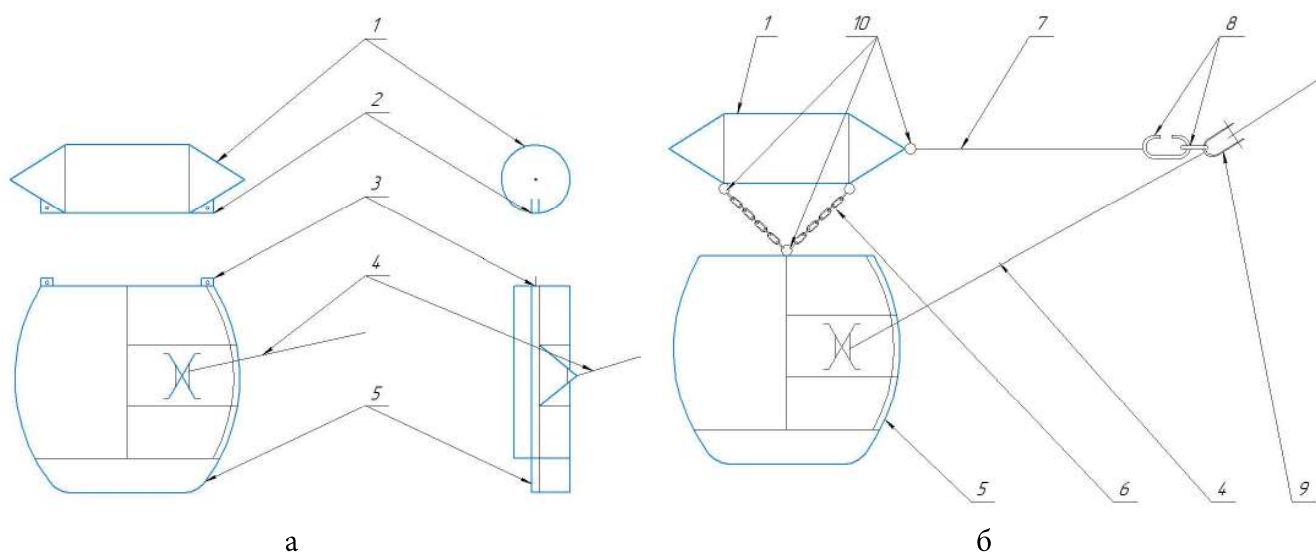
Крепление плавучего сегмента к траловой доске: а — жесткое; б — гибкое; 1 — плавучий сегмент; 2 — проушина; 3 — ухо; 4 — ваер; 5 — траловая доска; 6 — уздечка; 7 — удерживающий трос; 8 — разъемные звенья; 9 — скоба; 10 — рым
